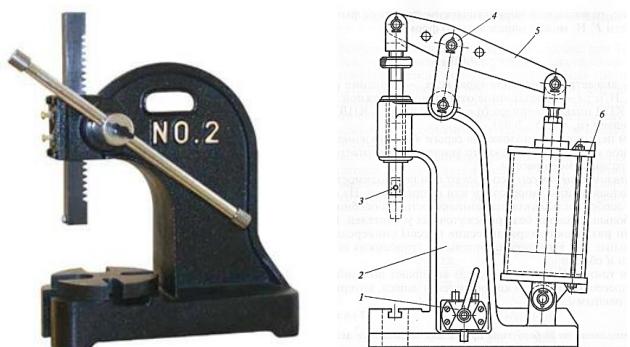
Реечный и пневматический прессы: 1 – распределительный кран; 2 – станина; 3 – пуансон; 4 – серьга; 5 – рычажный усилитель; 6 – пневмоцилиндр
